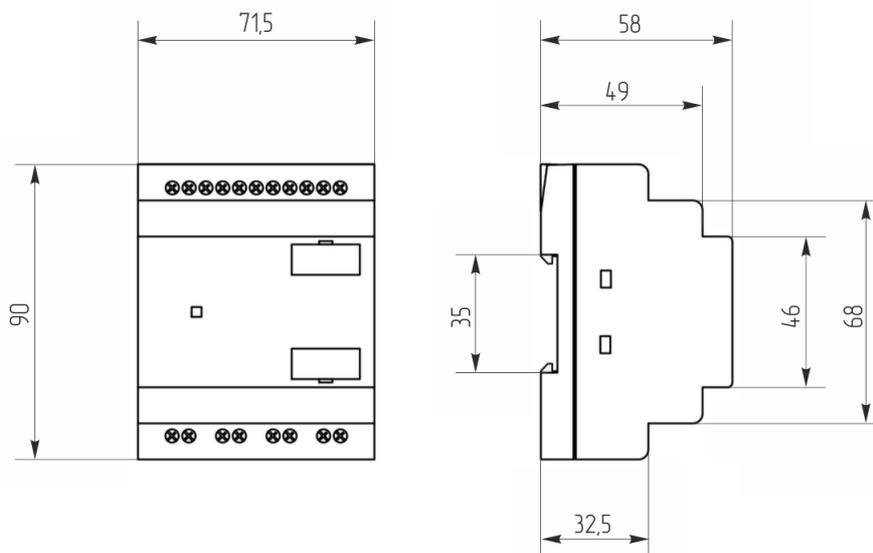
Габаритные и установочные размеры модуля ЦПУ
